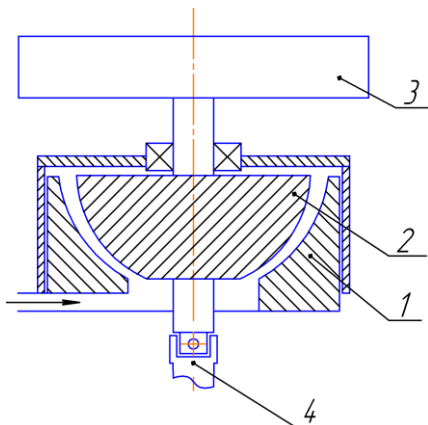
Схема газостатичного опорного механізму ударно-відцентрової дробарки
